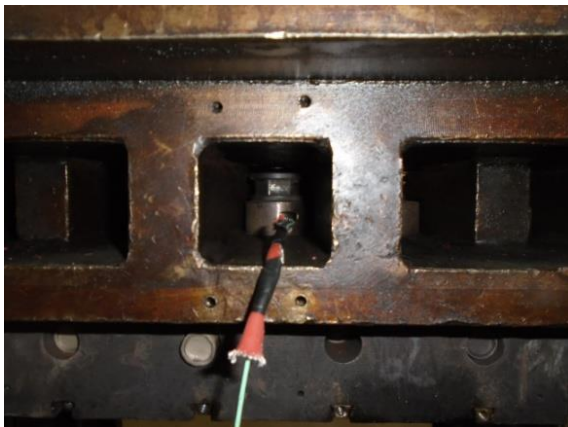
Molde após a instalação do “copo” para medição de força de prensagem.
